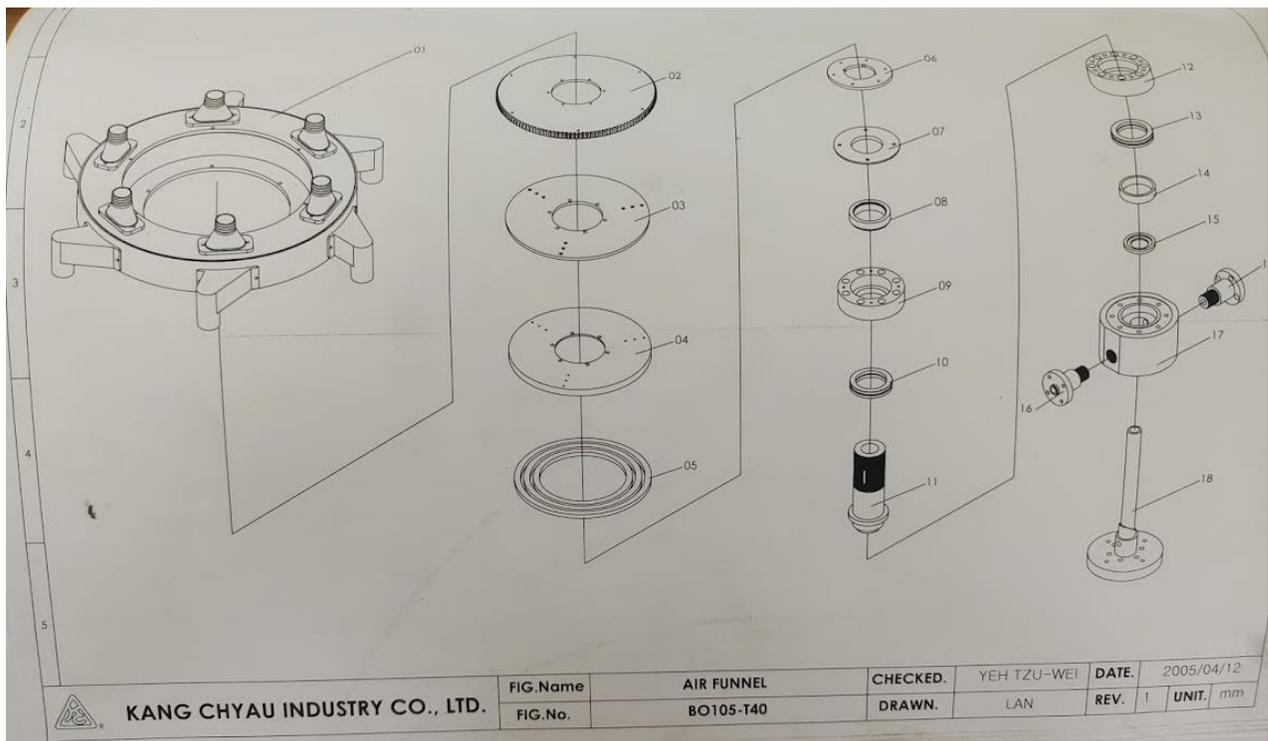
Despiece de bloque inferior máquina extrusora #1 y #2
